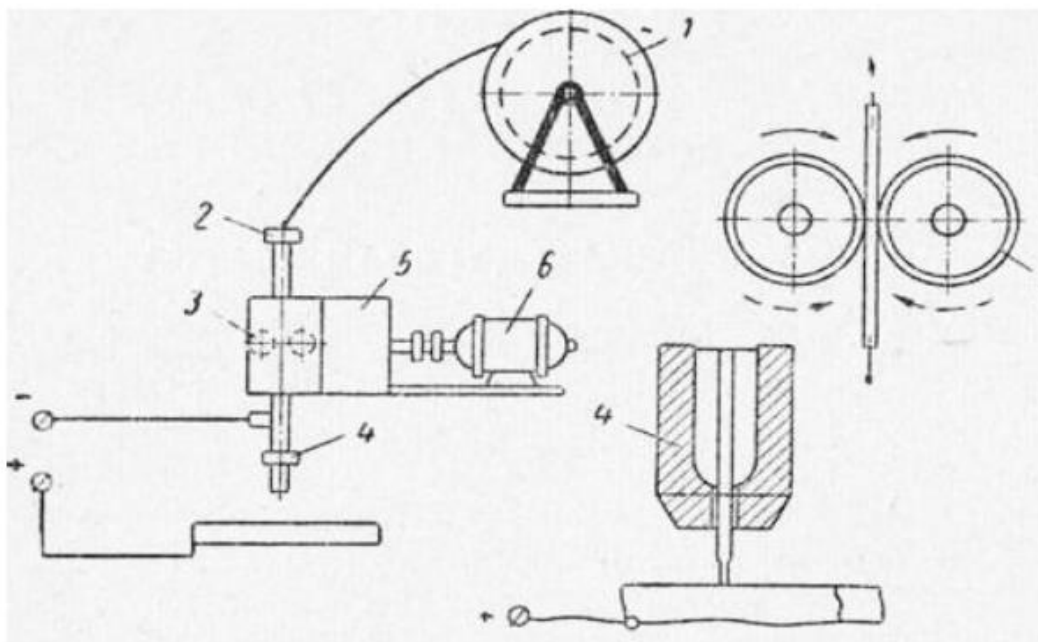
Схема автомата для дугового зварювання металевим електродом:
